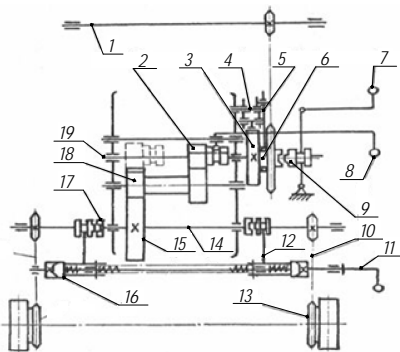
Схема механизма самопередвижения машины СМ-4:
